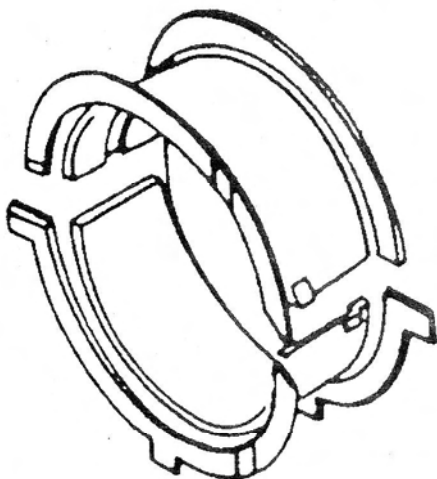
Правильная установка регулировочных полушайб осевого люфта коленчатого вала.
